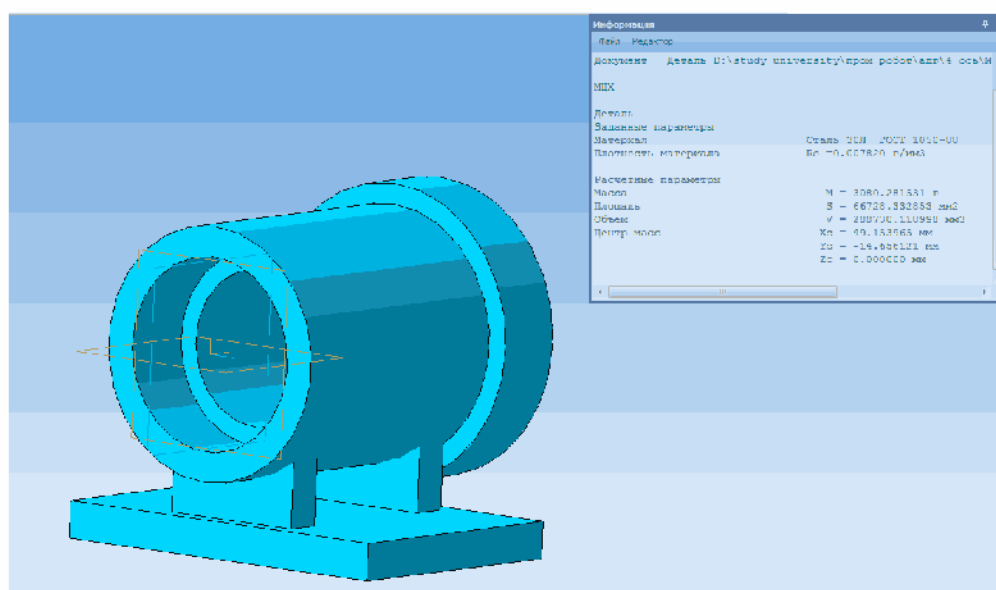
3d модель заготовки при литті в піщано-глинисті форми
